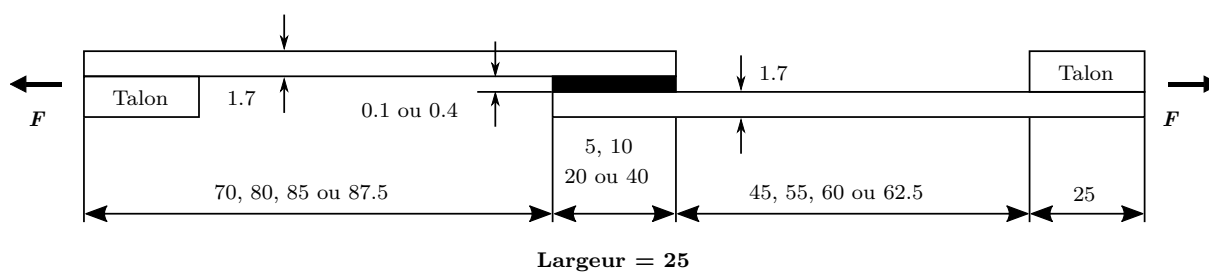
Géométrie des éprouvettes de simple recouvrement (pas à l'échelle, dimensions en mm).
